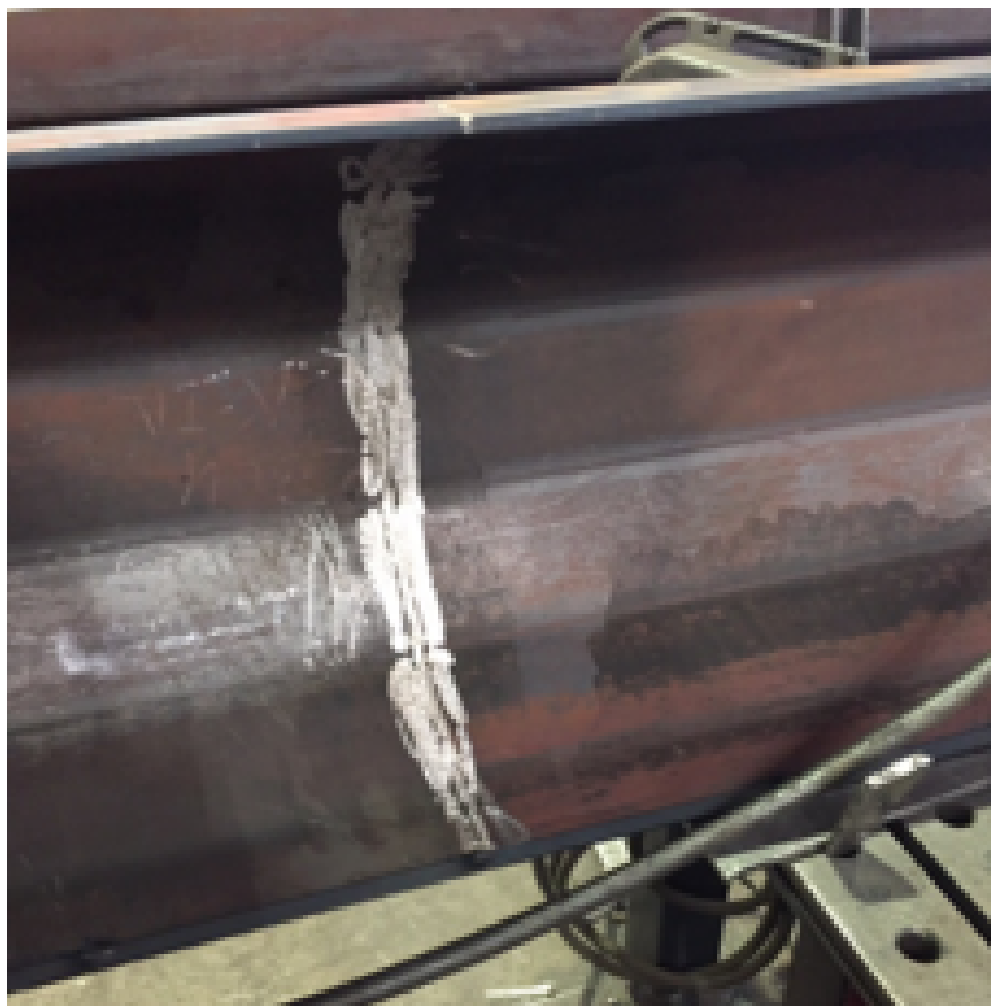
Зачистка после сварки нижних частей короба
